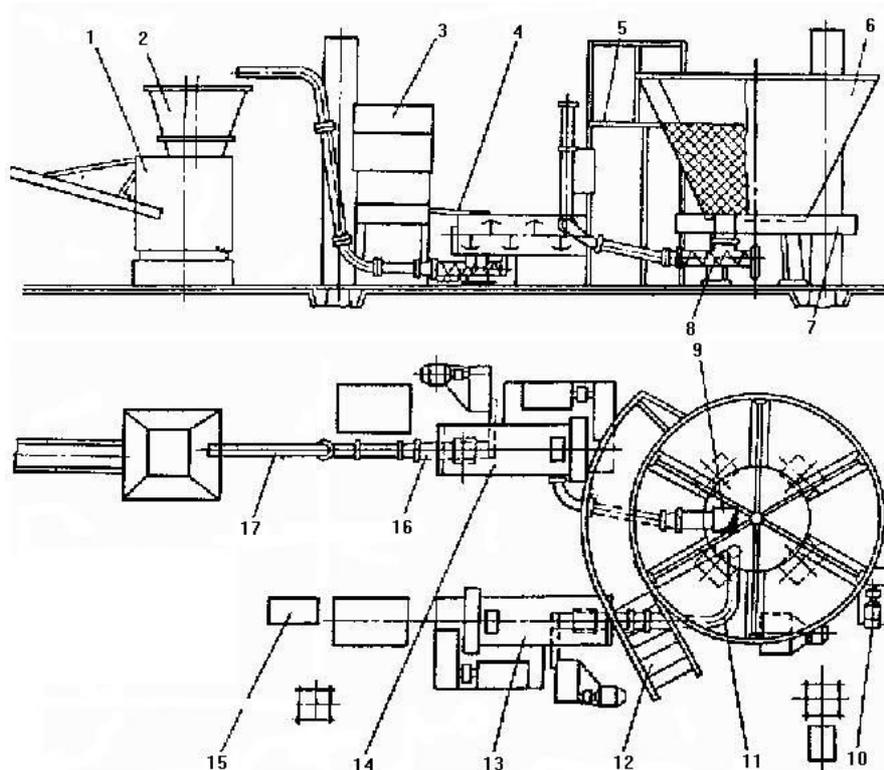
Тестоприготовительный агрегат И8-ХАГ-6:
